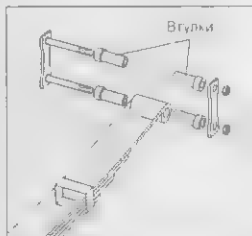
Листовые рессоры оборудованы резиновыми втулками
